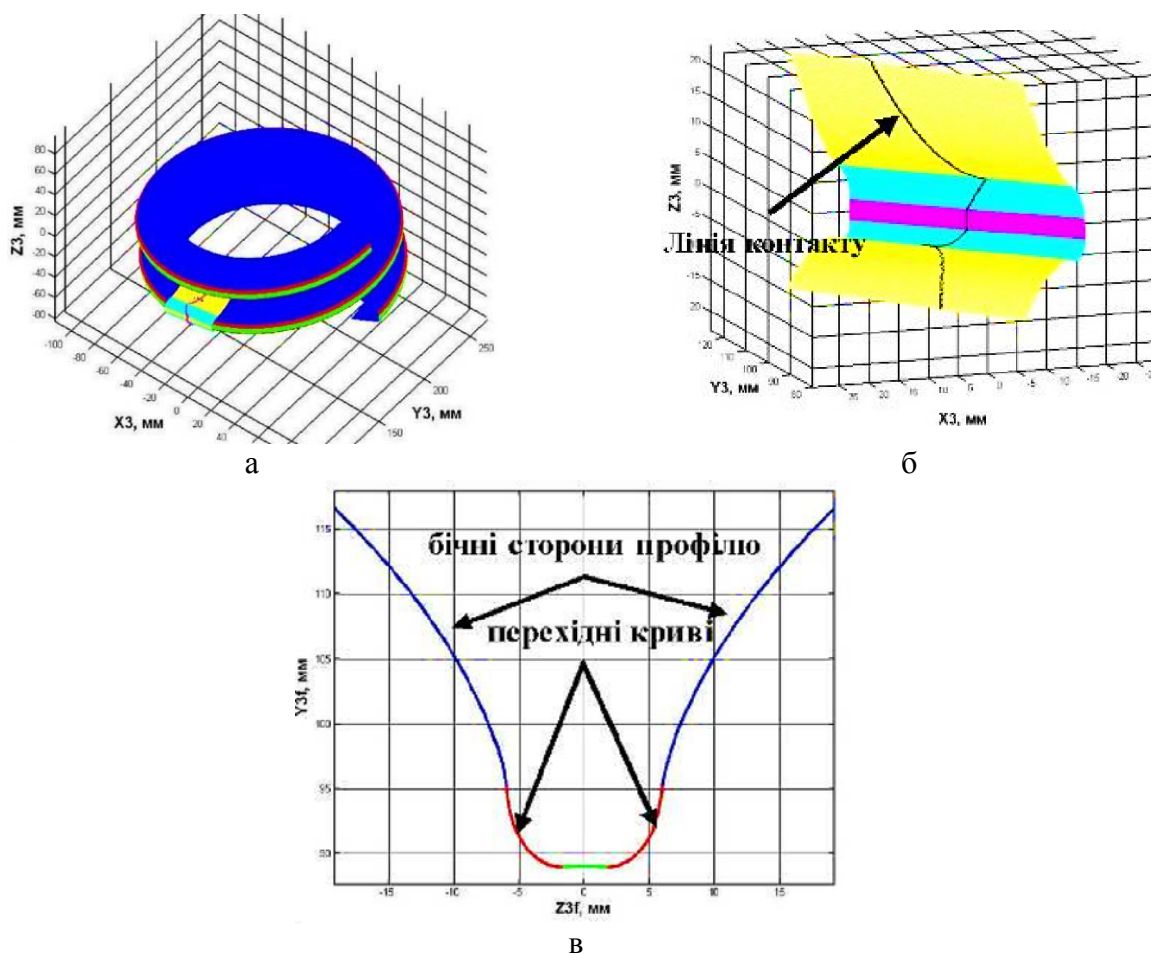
Розрахунок спряженої поверхні зубчастого колеса з ВП фрези:
